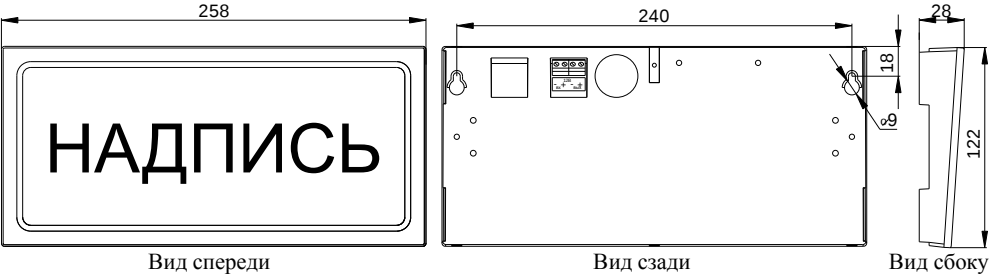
Внешний вид, габаритные и установочные размеры корпуса оповещателя
